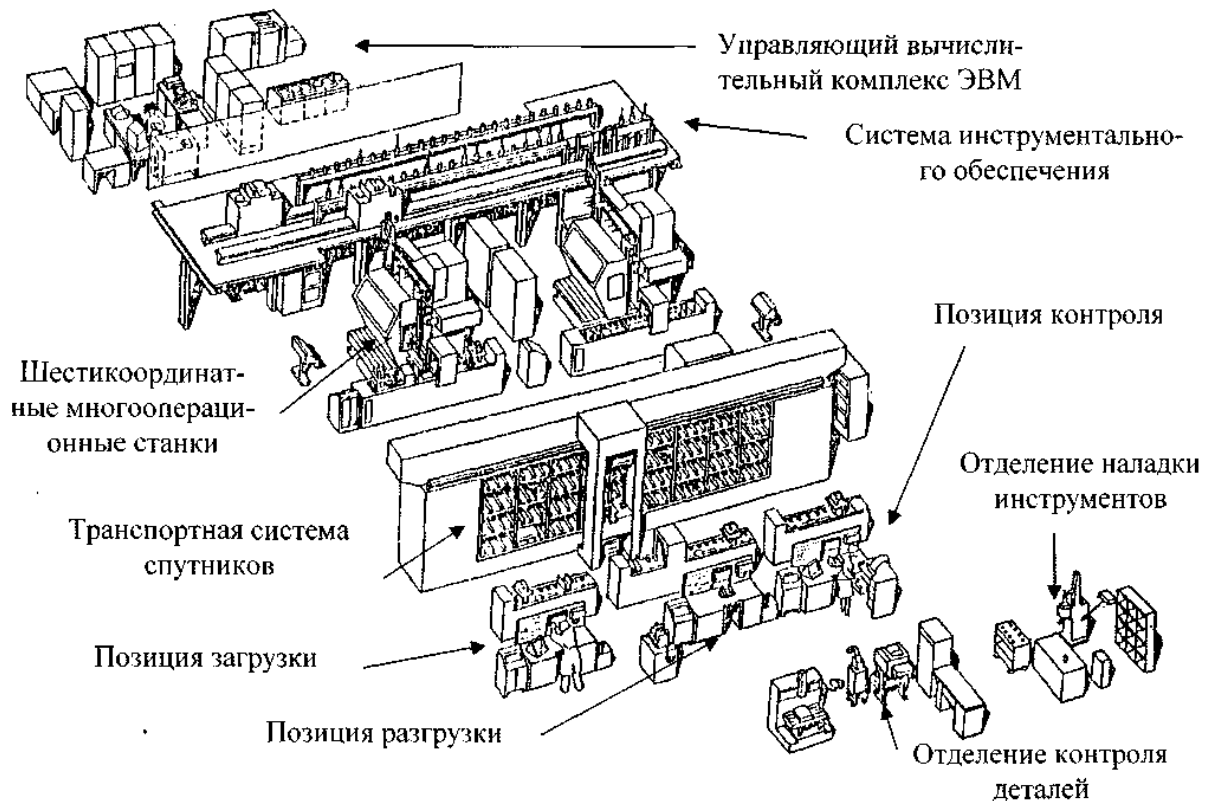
Гибкий автоматизированный комплекс для обработки корпусных деталей
